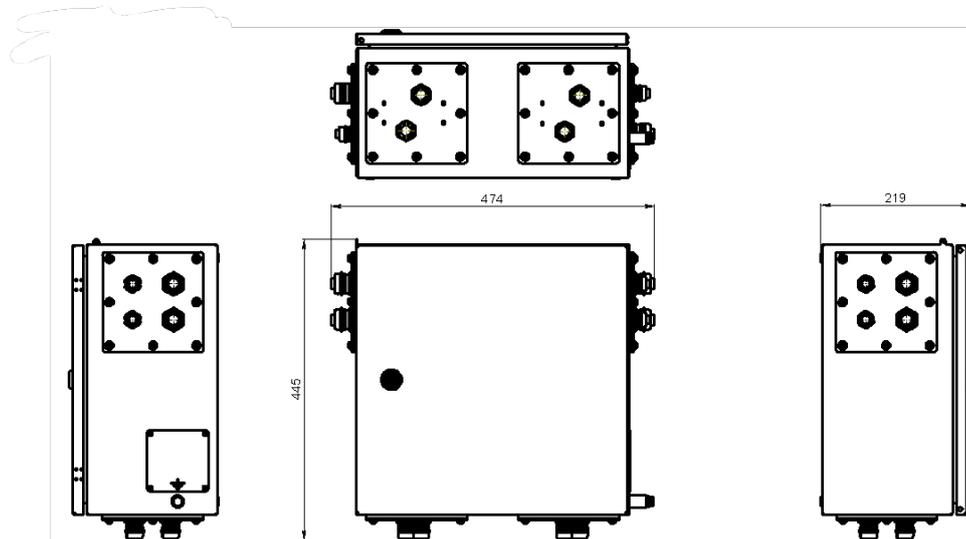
Внешний вид Коробки СПИН-ОС
